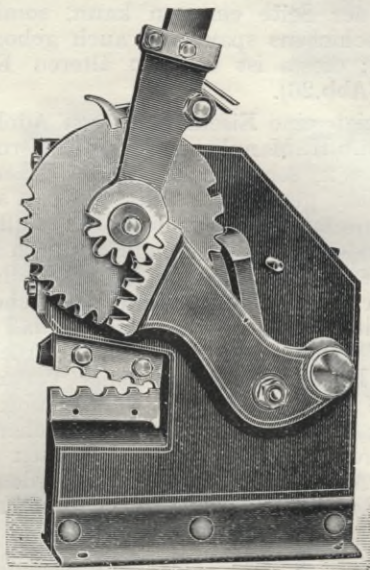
Schneidmaschine mit offen liegenden Messern.
